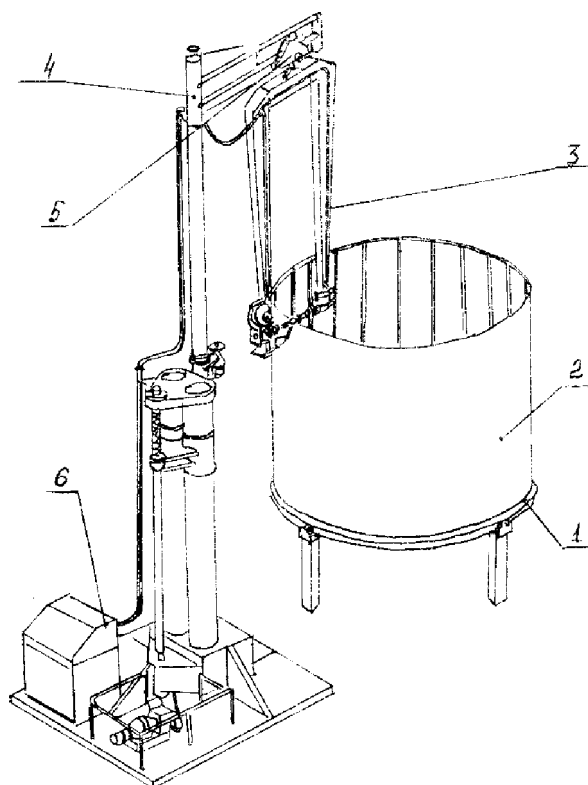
Схема доработочного автоматического рабочего места для доклепывания цилиндрических конструкций (ДАРМ-КЦ): 1 — поворотный стол; 2 — цилиндрическая клепаная конструкция; 3 — импульсный клепальный автомат; 4 — позиционер; 5 — узел подвески; 6 — пульт управления
